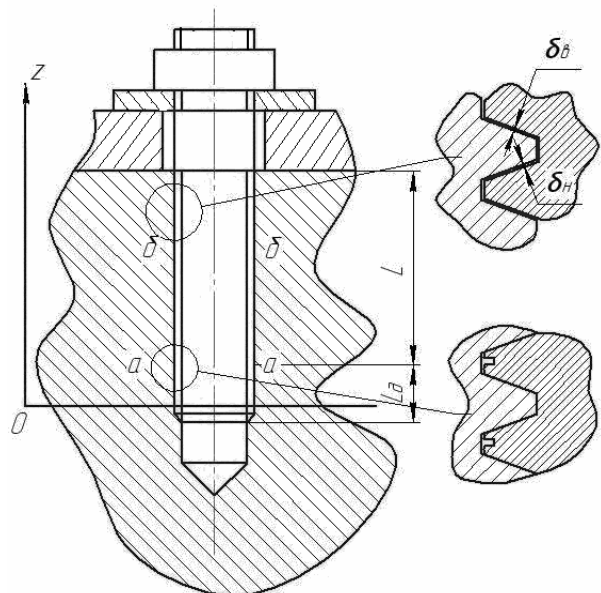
Резьбовыдавливающая шпилька с двумя участками посадочной части
